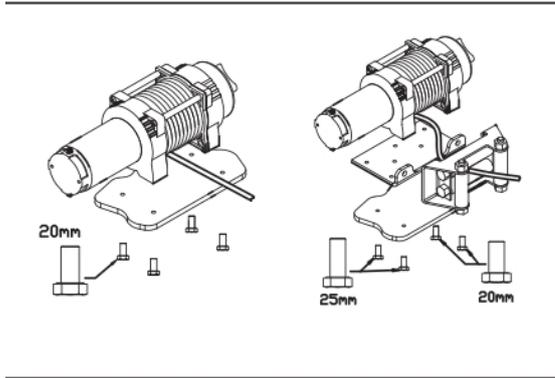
Ausrichtung der Hebebühne, Länge der Montageplatte und der Schrauben.
